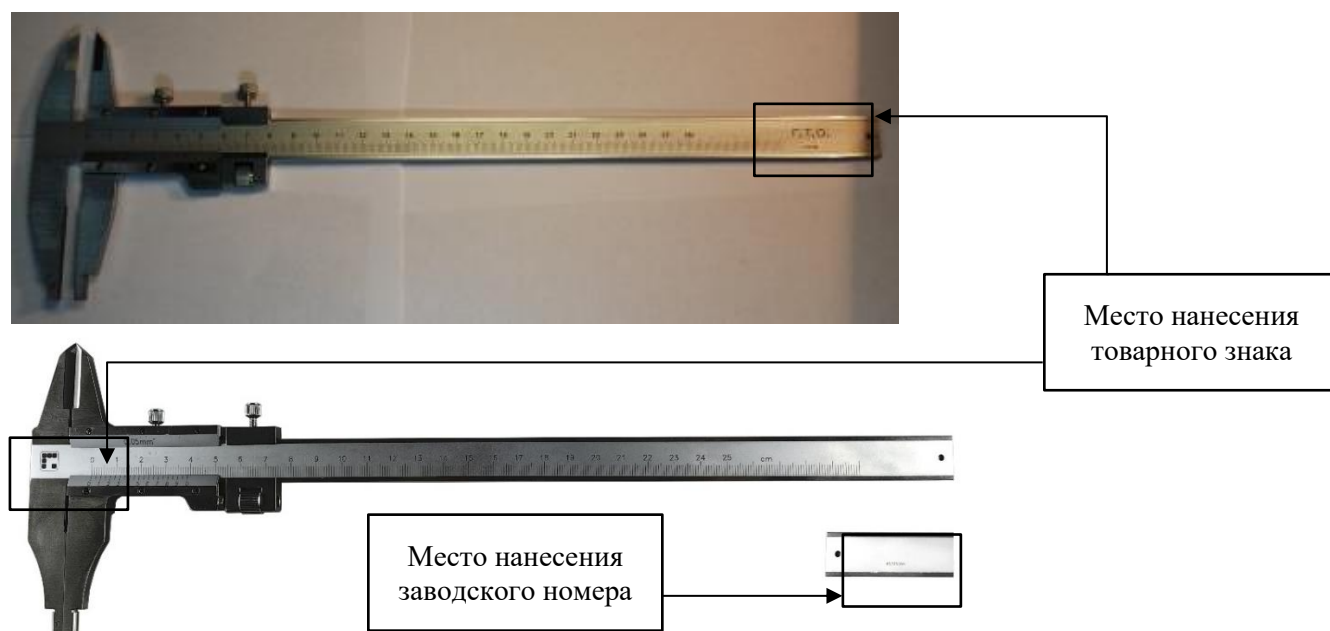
Общий вид штангенциркулей нониусных двухсторонних
